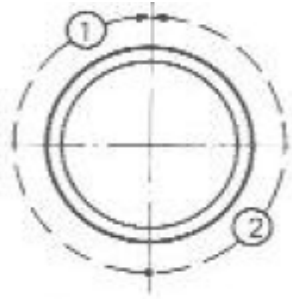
10 Soldadura vertical ascendente.
